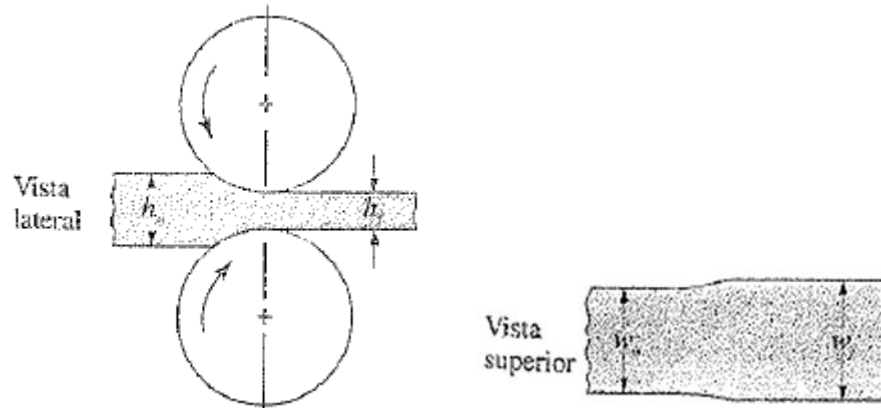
Ensanchado: incremento en el ancho de una tira en el laminado plano
